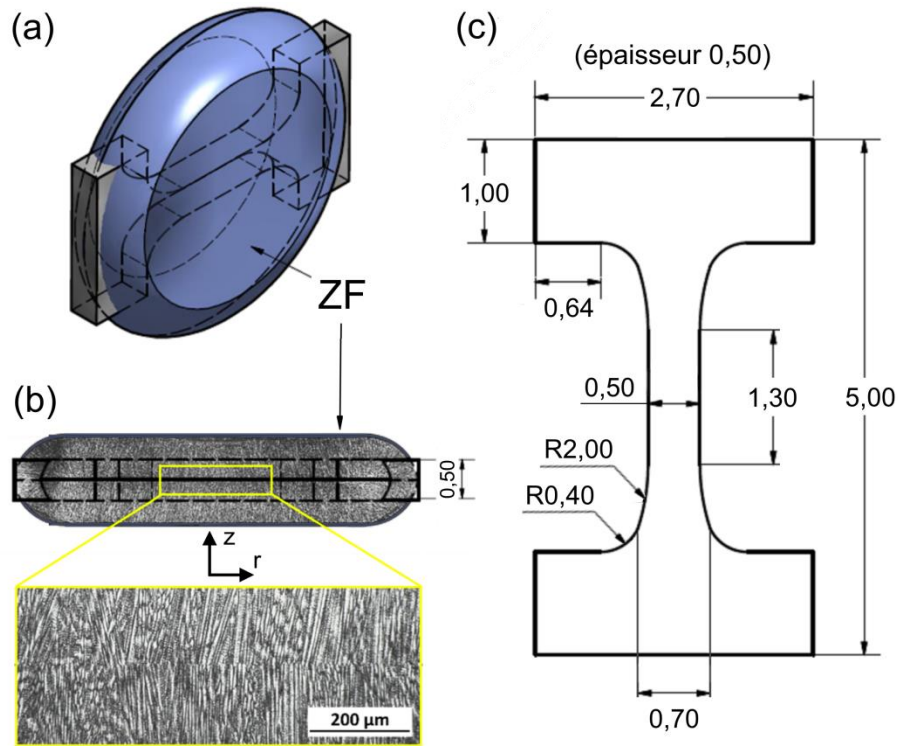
(a) Schéma d'une micro-éprouvette usinée dans la ZF d'une soudure, schématisée en bleu. (b) Orientation de la structure de solidification, révélée par attaque électrolytique à la soude, en relation avec l'éprouvette. (c) Dimensions en mm des micro-éprouvettes usinées.
